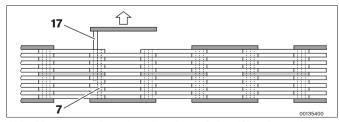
Lagerzapfen mit verbundener Schweißlasche entfernen
